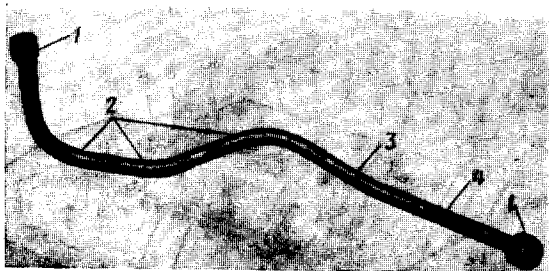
Инструментальный сборно-разборный макет-эталон из стандартных элементов:
